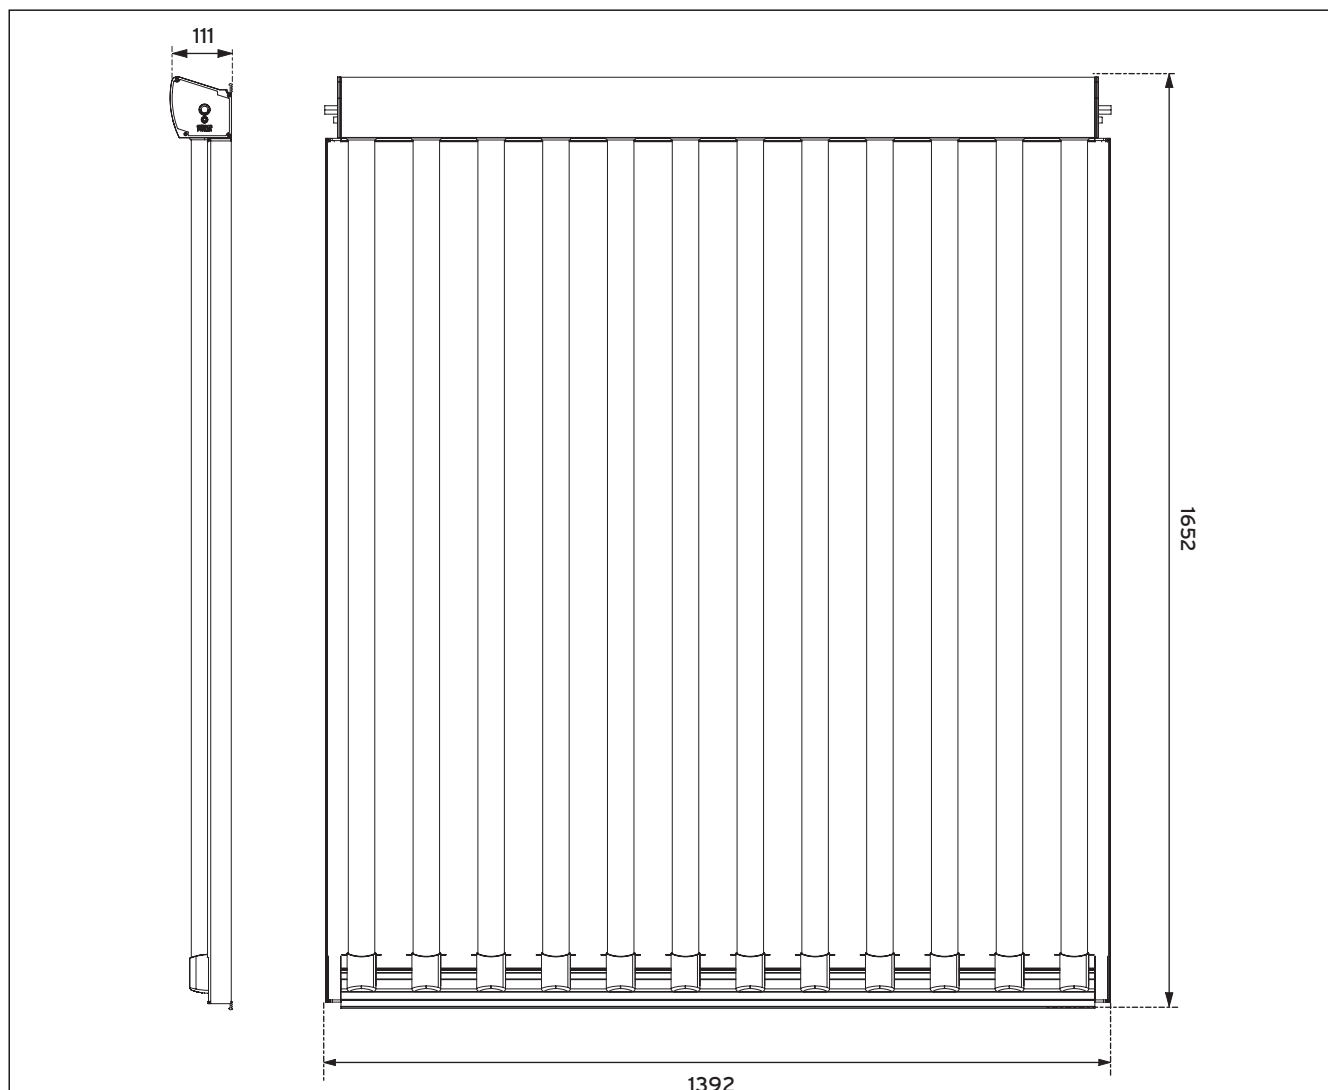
Dessin de dimensionnement VTK 1140/2
